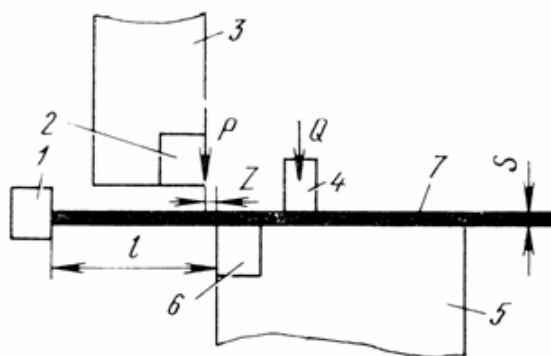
Схема резания листа на гильотинных ножницах: 1 – упор; 2 – верхний нож; 3 – ползун гильотинных ножниц; 4 – прижим; 5 – стол; 6 – нижний нож; 7 – заготовка
